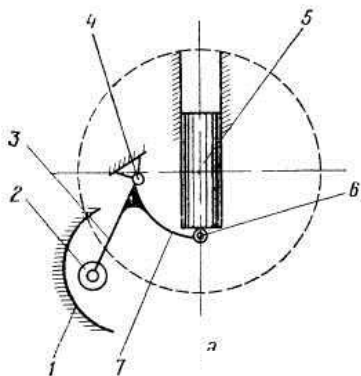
Схема приводу виштовхувача тістоподільної машини РМК: 1 – ексцентриковий механізм; 2 – ролик; 3, 7 – важелі; 4 – вал; 5 – поршень; 6 – обмежник
